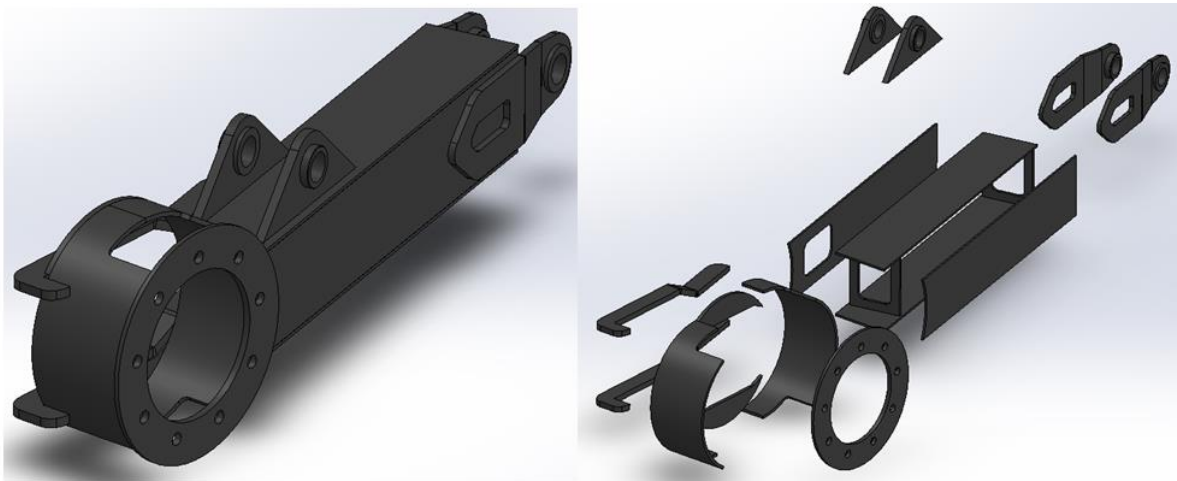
Detalle de las piezas en las que se compone modulo soldado de la pata motriz izquierda.
